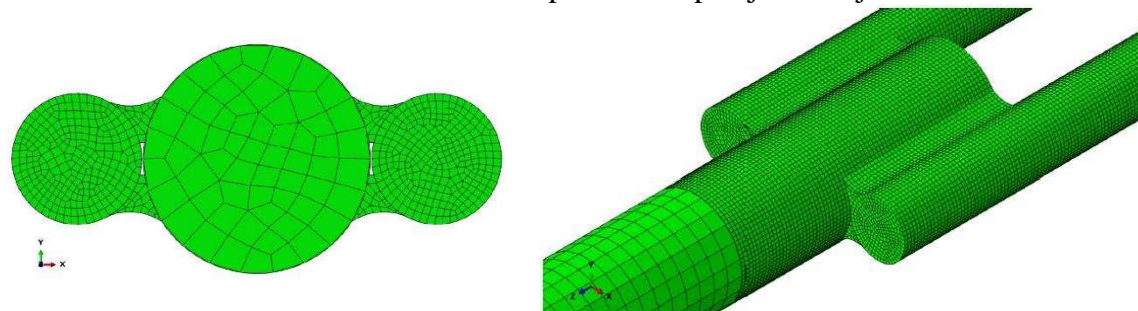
Vista frontal y en perspectiva de las uniones soldadas del modelo G – M3 con presencia de Socavación.
